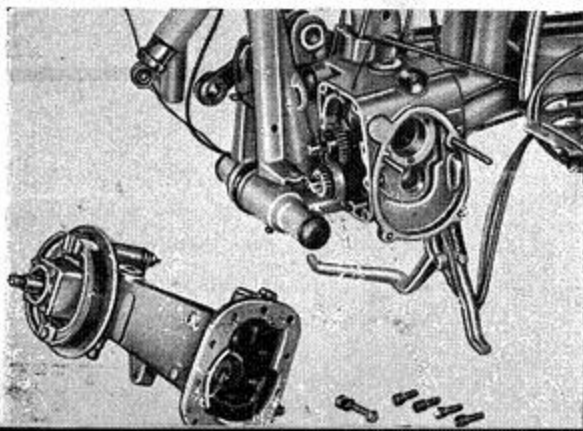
Desmontaje del amortiguador tubular y grupo de transmisión.
